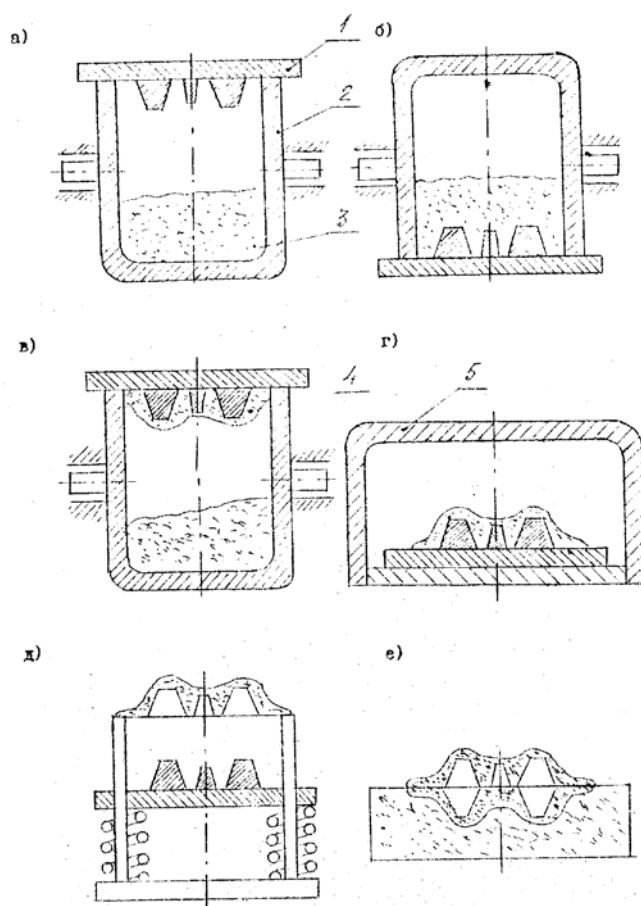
Схема технологического процесса изготовления отливки в оболочковой форме
